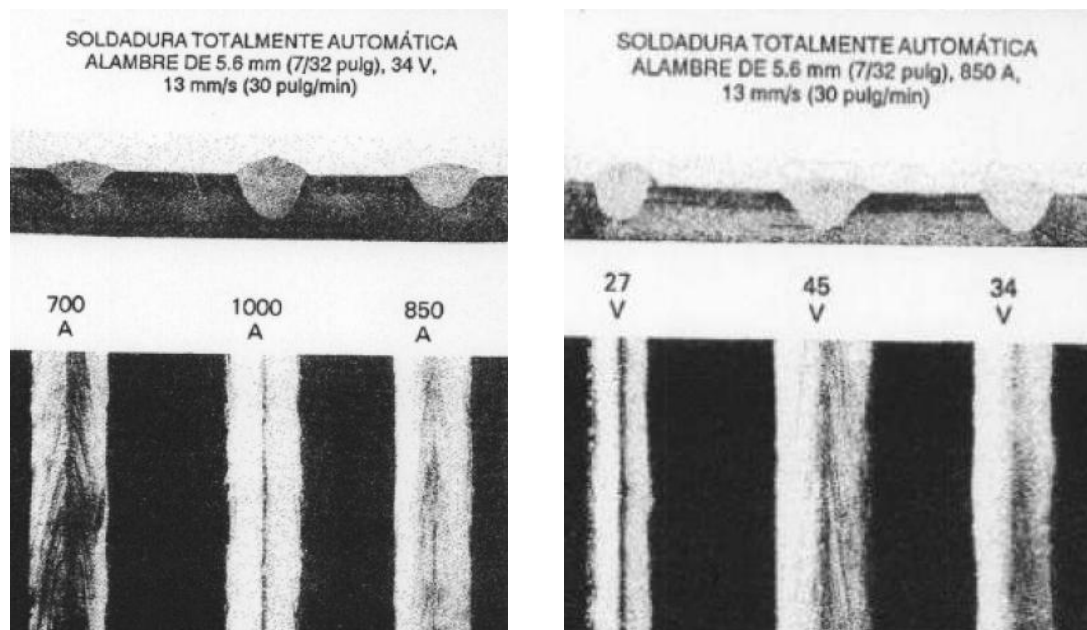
Relación del amperaje y la anchura del cordón de soldadura en el proceso SAW. [22]
